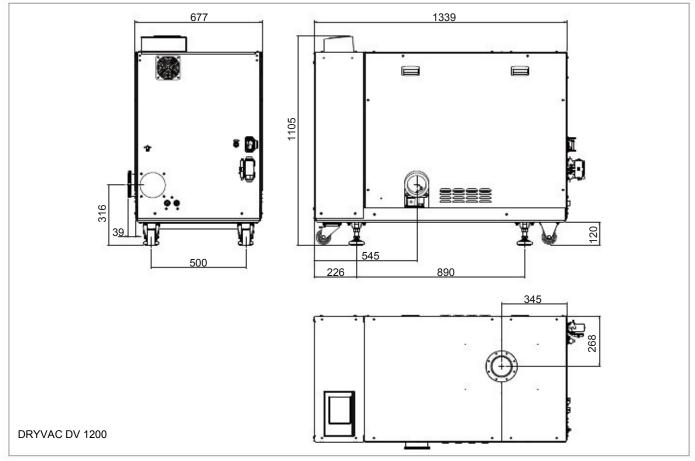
Disegno dimensionale, dimensioni in  $\operatorname{mm}$
